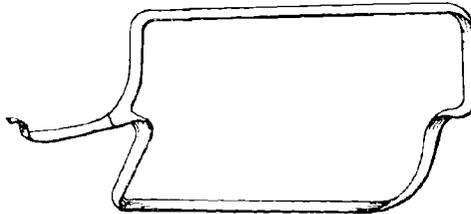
Section d'induit en tambour faite sur gabarit (Eickemeyer).
